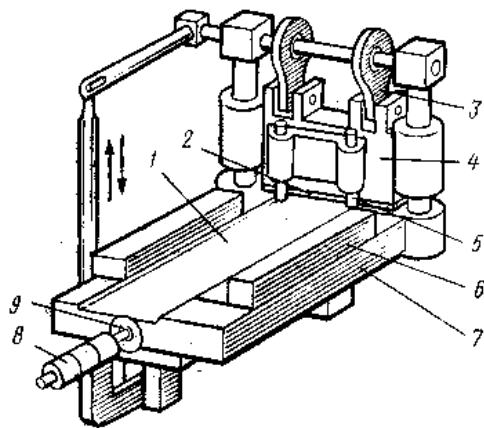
Механизированные гильотинные ножницы для резки стальных пластин: 1 — стальная лента; 2 — неподвижный нож гильотины; 3 — эксцентриковый привод вертикального подвижного ножа; 4 — подвижной нож; 5 — прижимы стальной ленты при ее резке на пластины; 6 — направляющие стальной ленты; 7 — станина; 8 — микрометр; 9 — упор микрометра, устанавливающий размер стальной ленты
